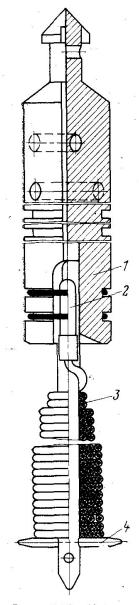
Торпеда корпусная из детонирующего шнура типа ТКДШ
